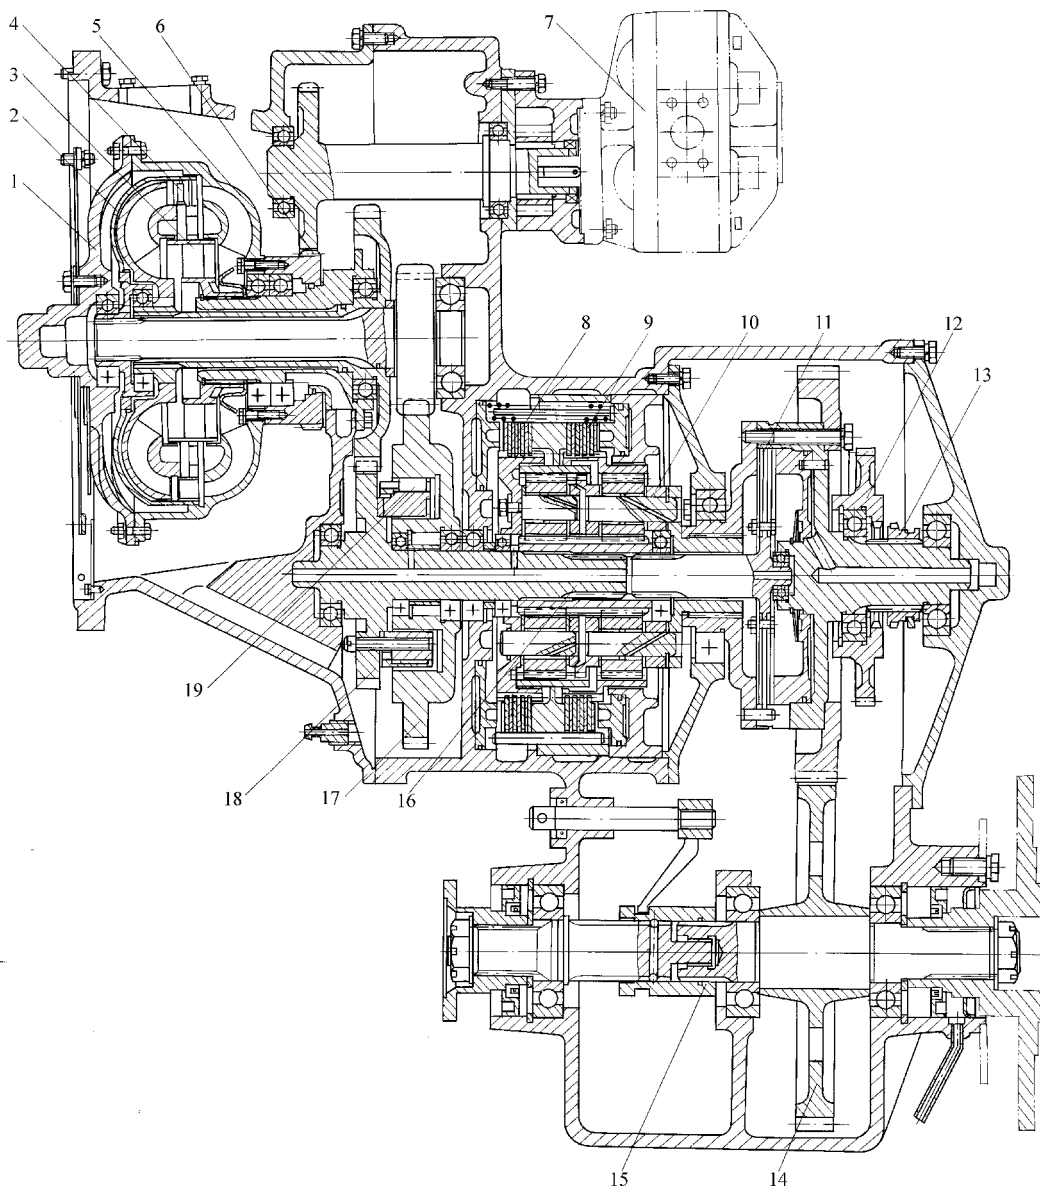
ZL40/50 液力机械传动装置结构简图
